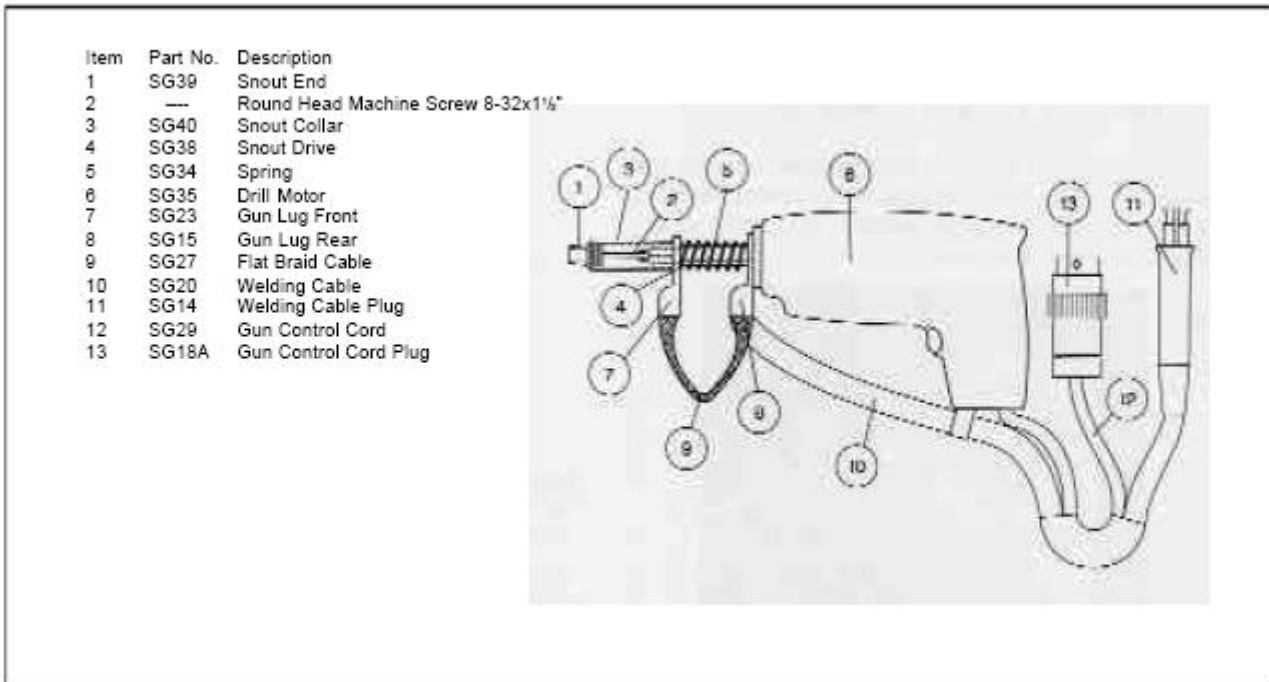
Lista de Partes de la Pistola de Soldadura.
